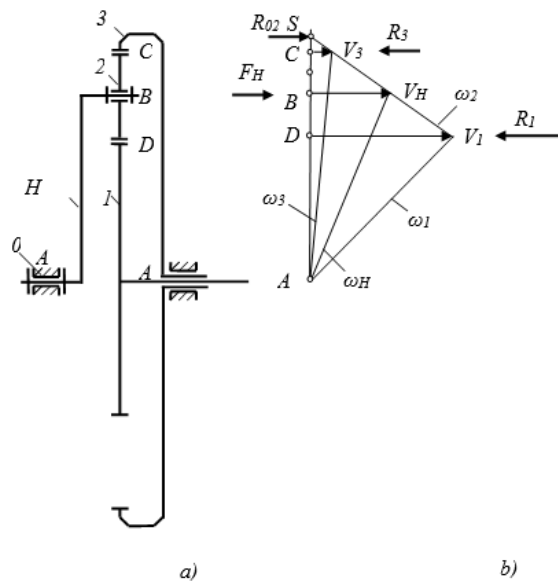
Двухподвижный зубчатый дифференциальный механизм
